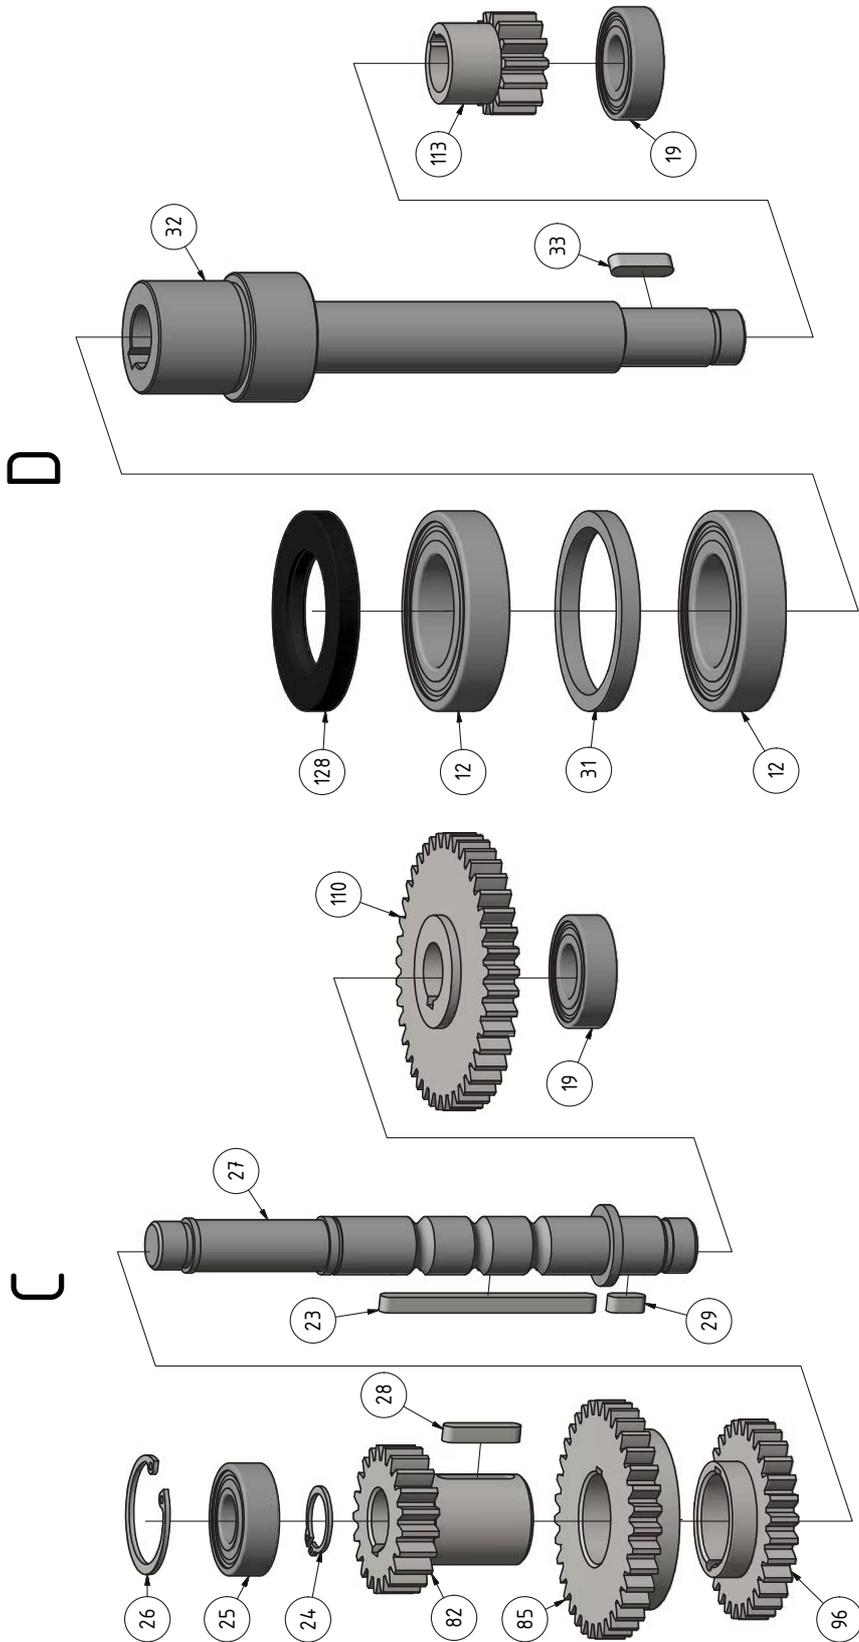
Fräskopf 3 von 6 - Milling head 3 von 6
